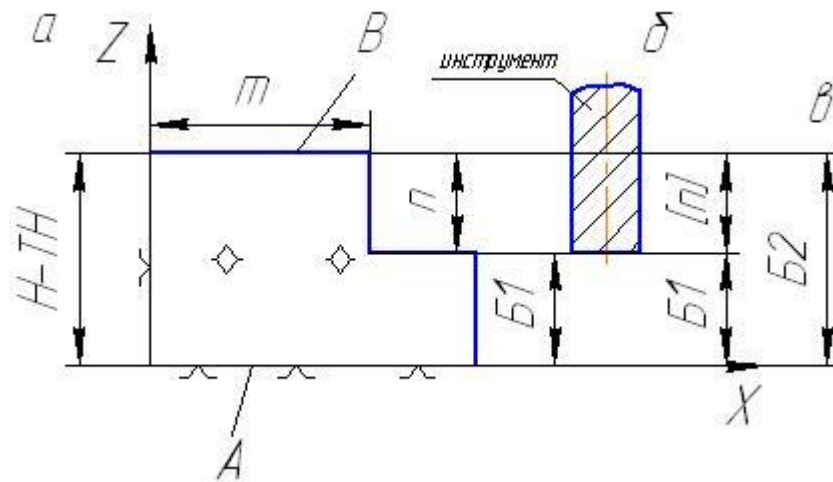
Схема к определению погрешности базирования: а) схема базирования детали; б) настройка инструмента при выполнении размера; в) размерная цепь (для размера  $n$ )
